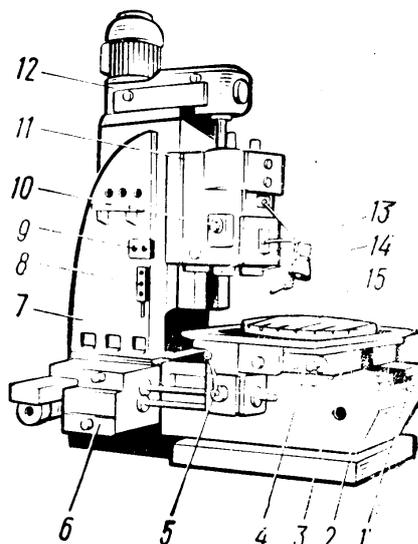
Карусельно-фрезерный станок мод. 621М:
